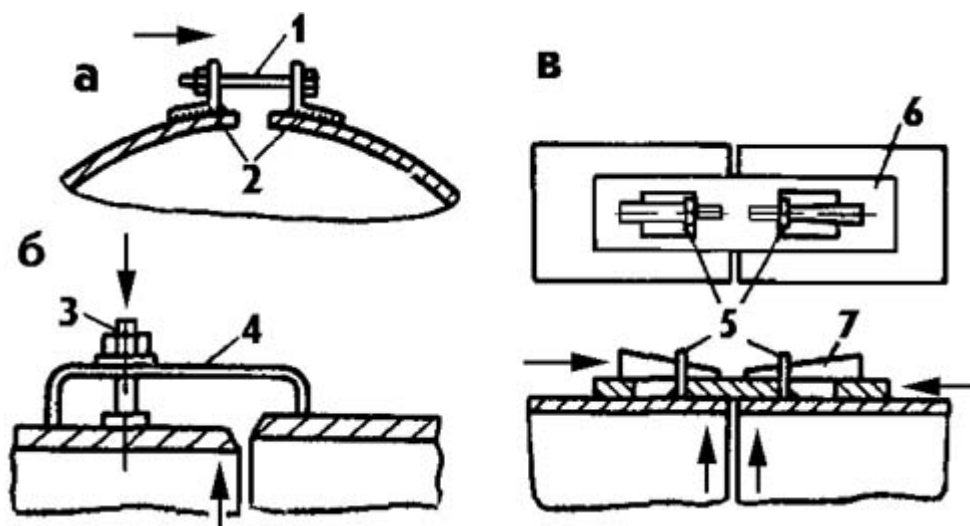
Натяжні пристосування для підготовки обичайки під зварювання.
